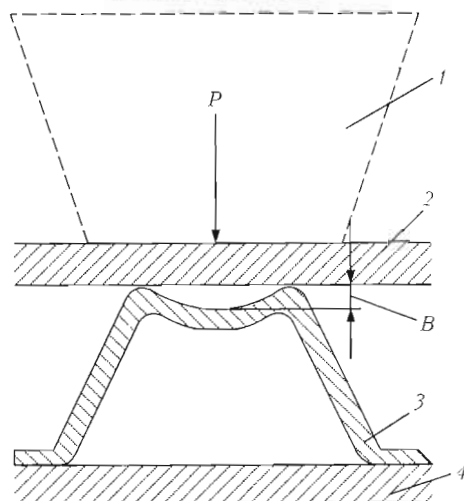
Схема образования зазора B в месте выполнения ДТС трехслойной панели: 1 — сварочная горелка; 2, 4 — обшивка панели; 3 — ячеистый наполнитель
